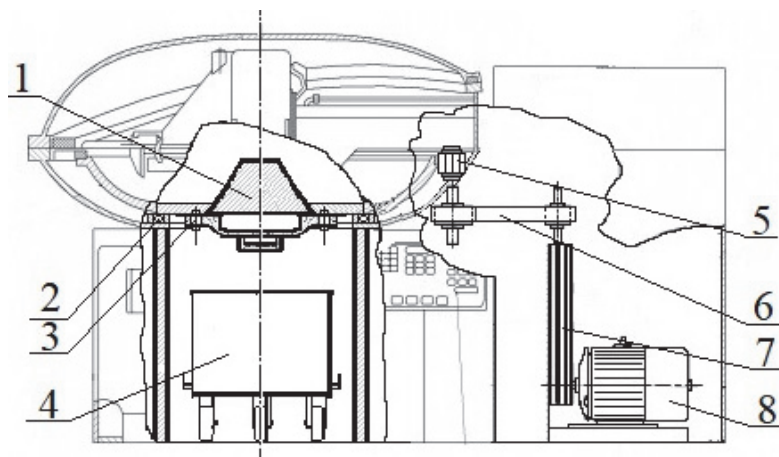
Выгрузочный люк и вращательный узел чаши: 1 – выгрузочный люк; 2 – подшипник качения; 3 – области крепления люка; 4 – передвижной созреватель; 5 – ролик из плотного силикона; 6 – ремённая передача; 7 – клиноременная передача; 8 – привод
